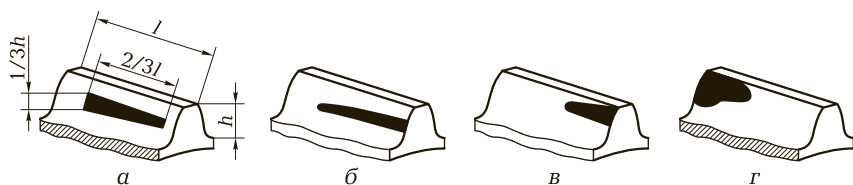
Расположение пятен контакта при контроле сборки конических зубчатых колес с прямым зубом:
